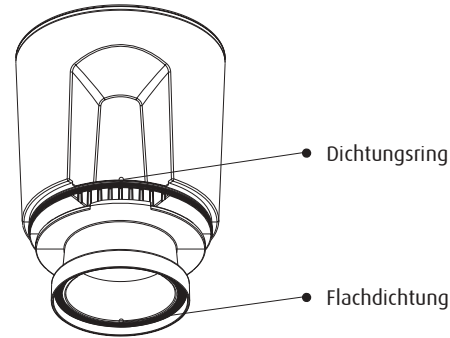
Schaumbehälter – O-Ring und Flachdichtung
